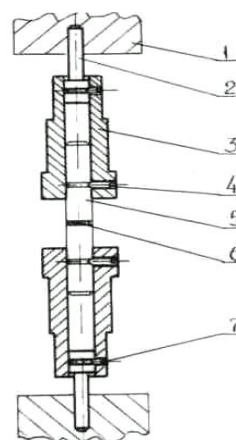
Схема пристрою для визначення адгезійної міцності покриттів, з'єднаних встик: 1 – затискач; 2 – державка; 3 – обойма; 4 – гвинт; 5 – зразок; 6 – покриття; 7 – фіксатор.
